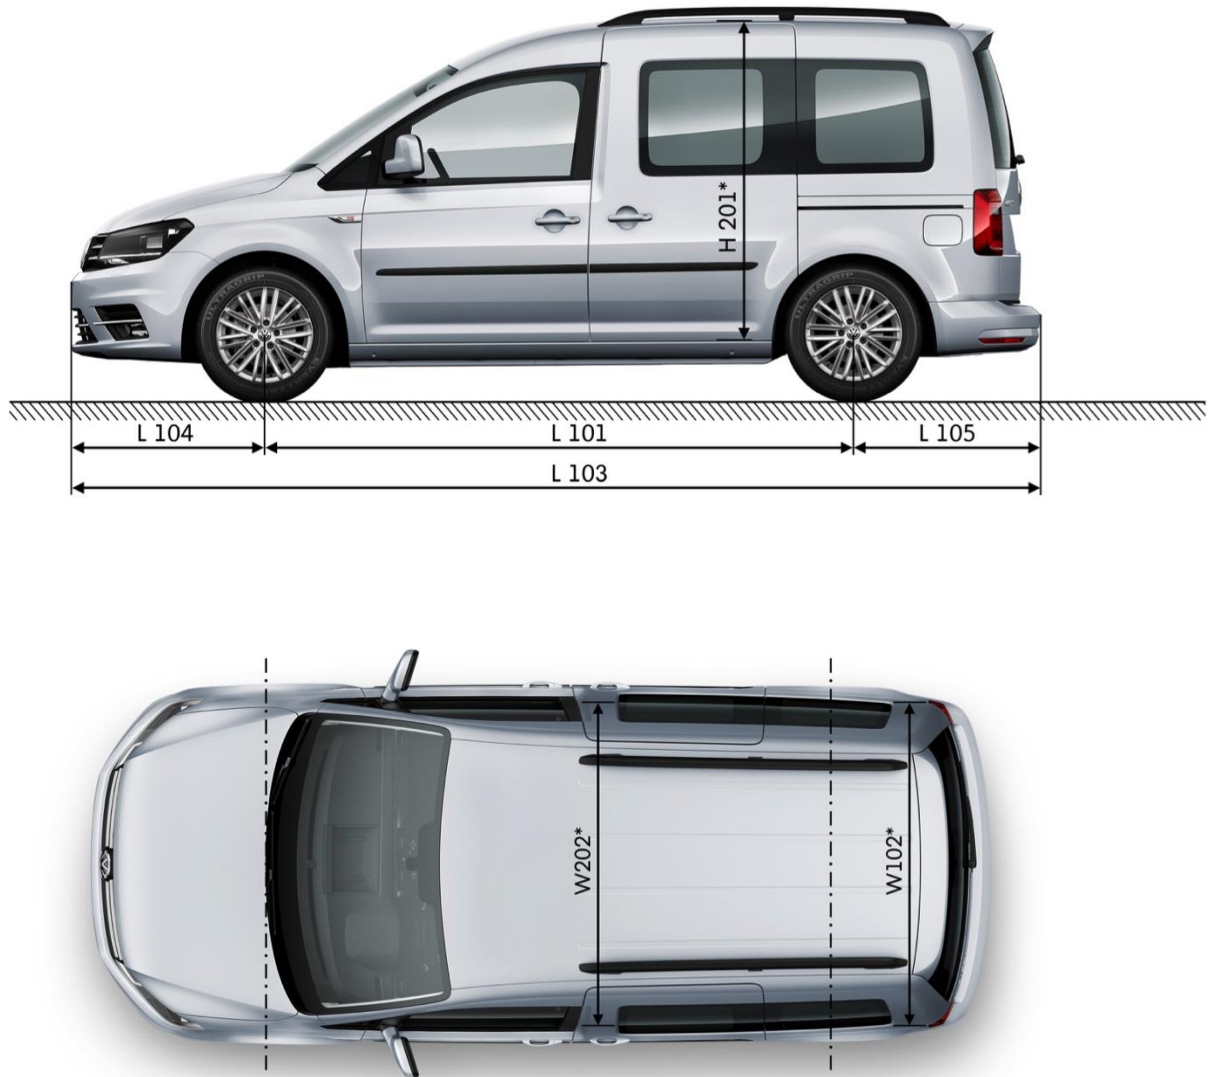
Габариты Caddy (согласно стандарту DIN 70020, ч. 1)
